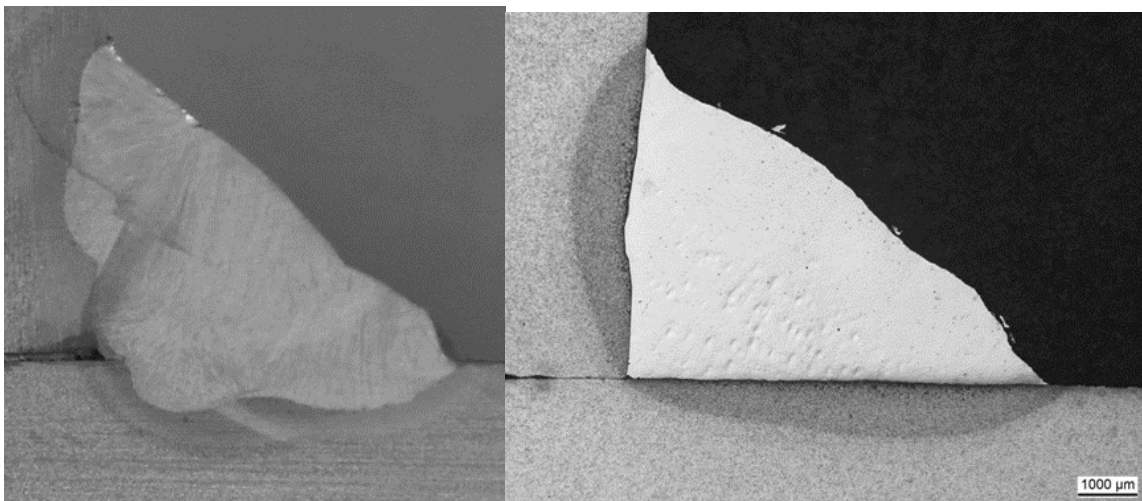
Schweißnaht (links) und Lotnaht (rechts) [79]
